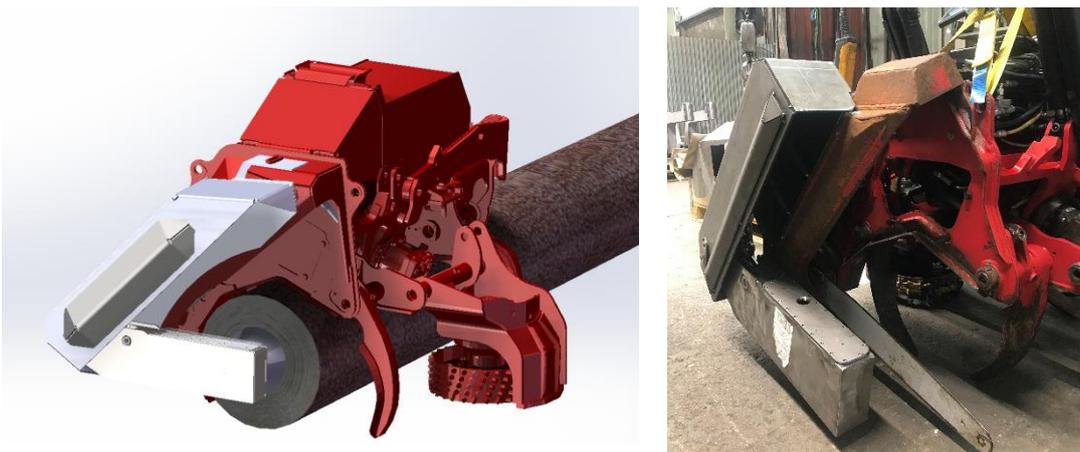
Kamerasystem im CAD am PC und in der Fertigung
